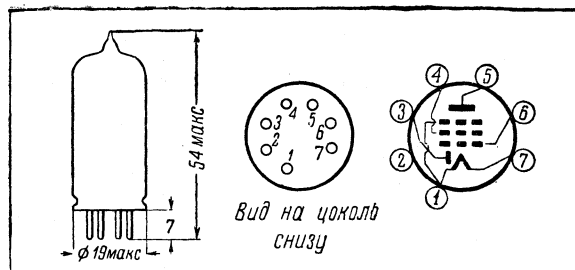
Общий вид и схема цоколевки лампы 1Б1П
